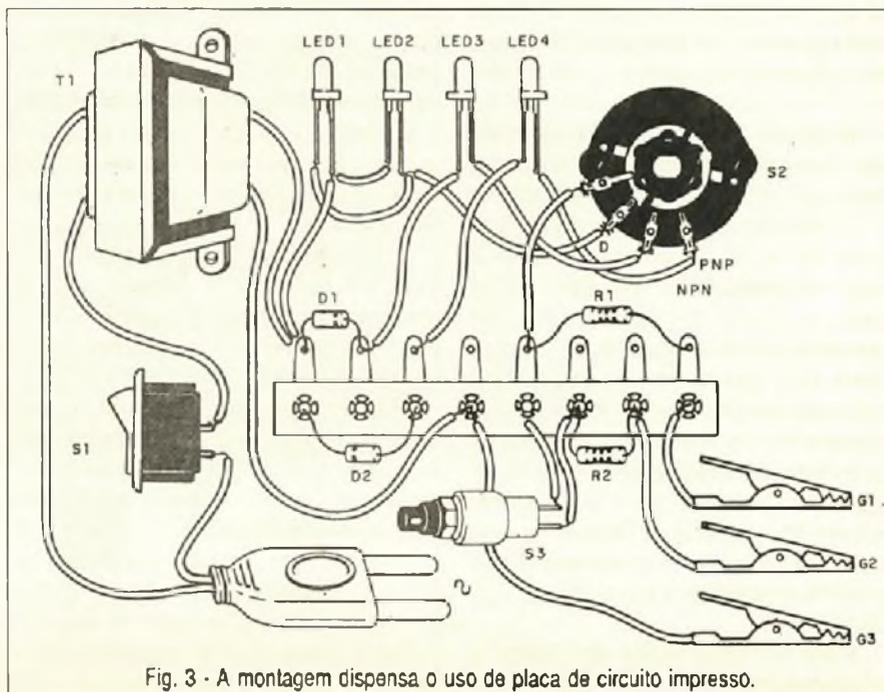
A montagem dispensa o uso de placa de circuito impresso.
